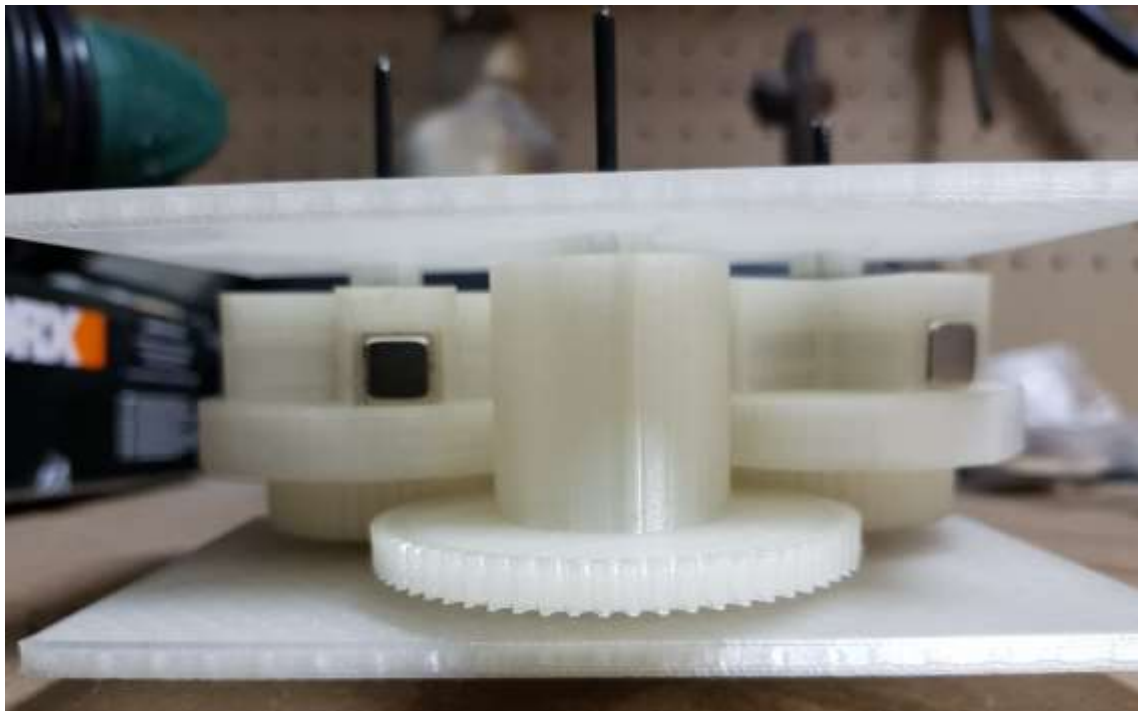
Montaje del VIM rotor-rotor con enlace mecánico.
